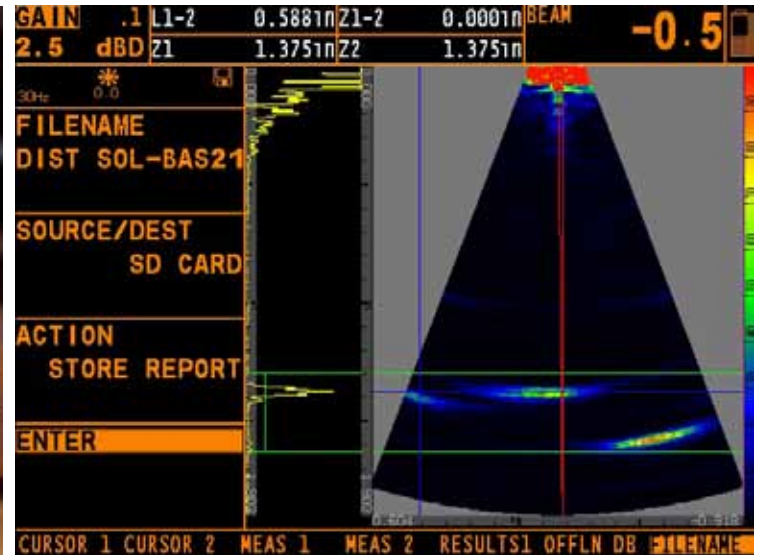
Imagen del Barrido Sectorial con el cursor a -0.5° , tocando el borde donde termina la fusión de la soldadura.
